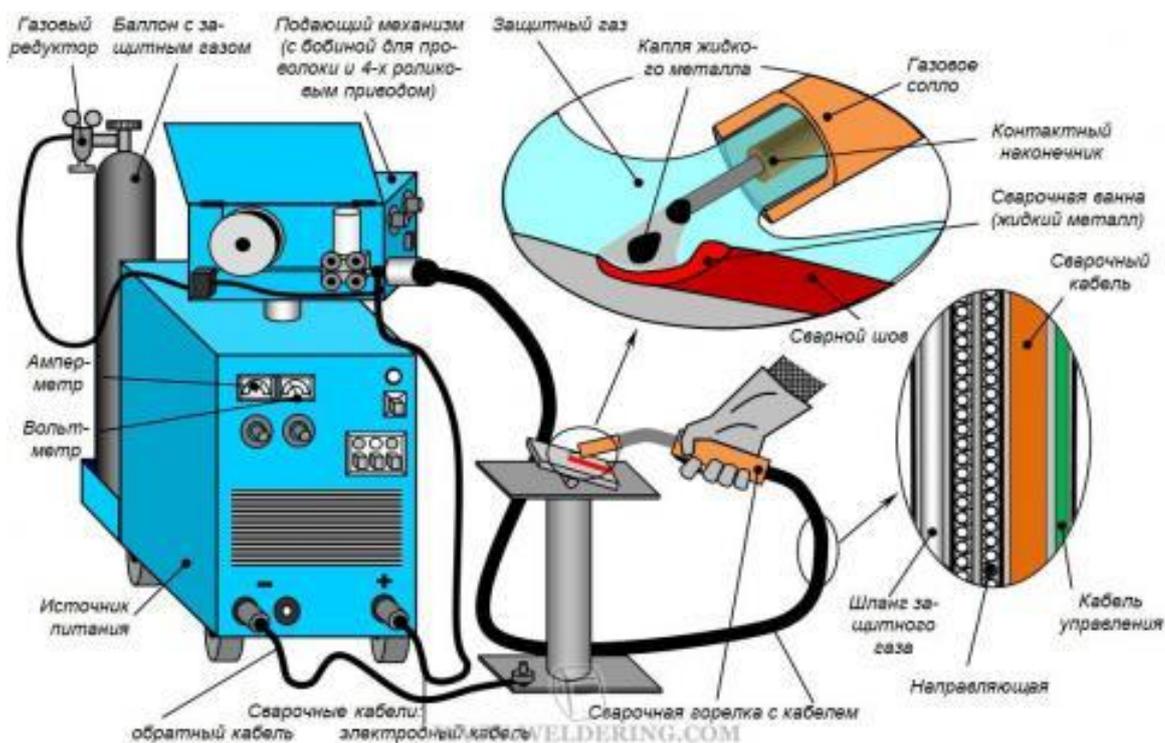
Оборудование для сварки в защитном газе
